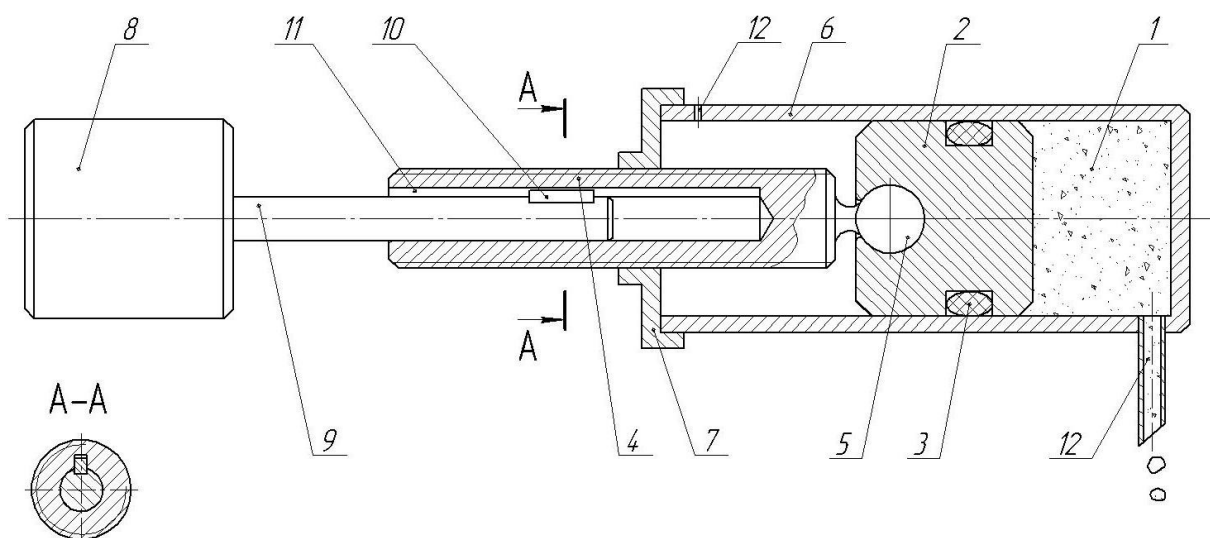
Конструкція краплинного дозатора для введення присадок
